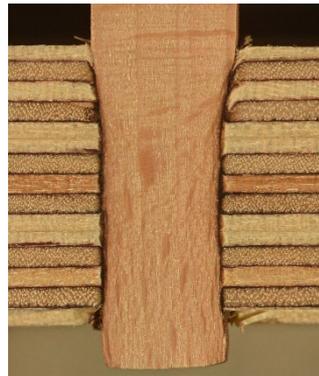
Verschweißte Holzschichten, © Wood Vision Lab
